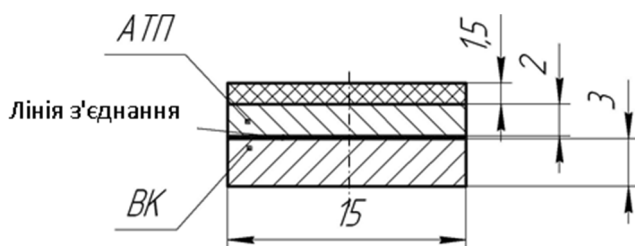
Ескіз типового вузла АТП збільшеної висоти, шляхом з'єднання з твердим сплавом
